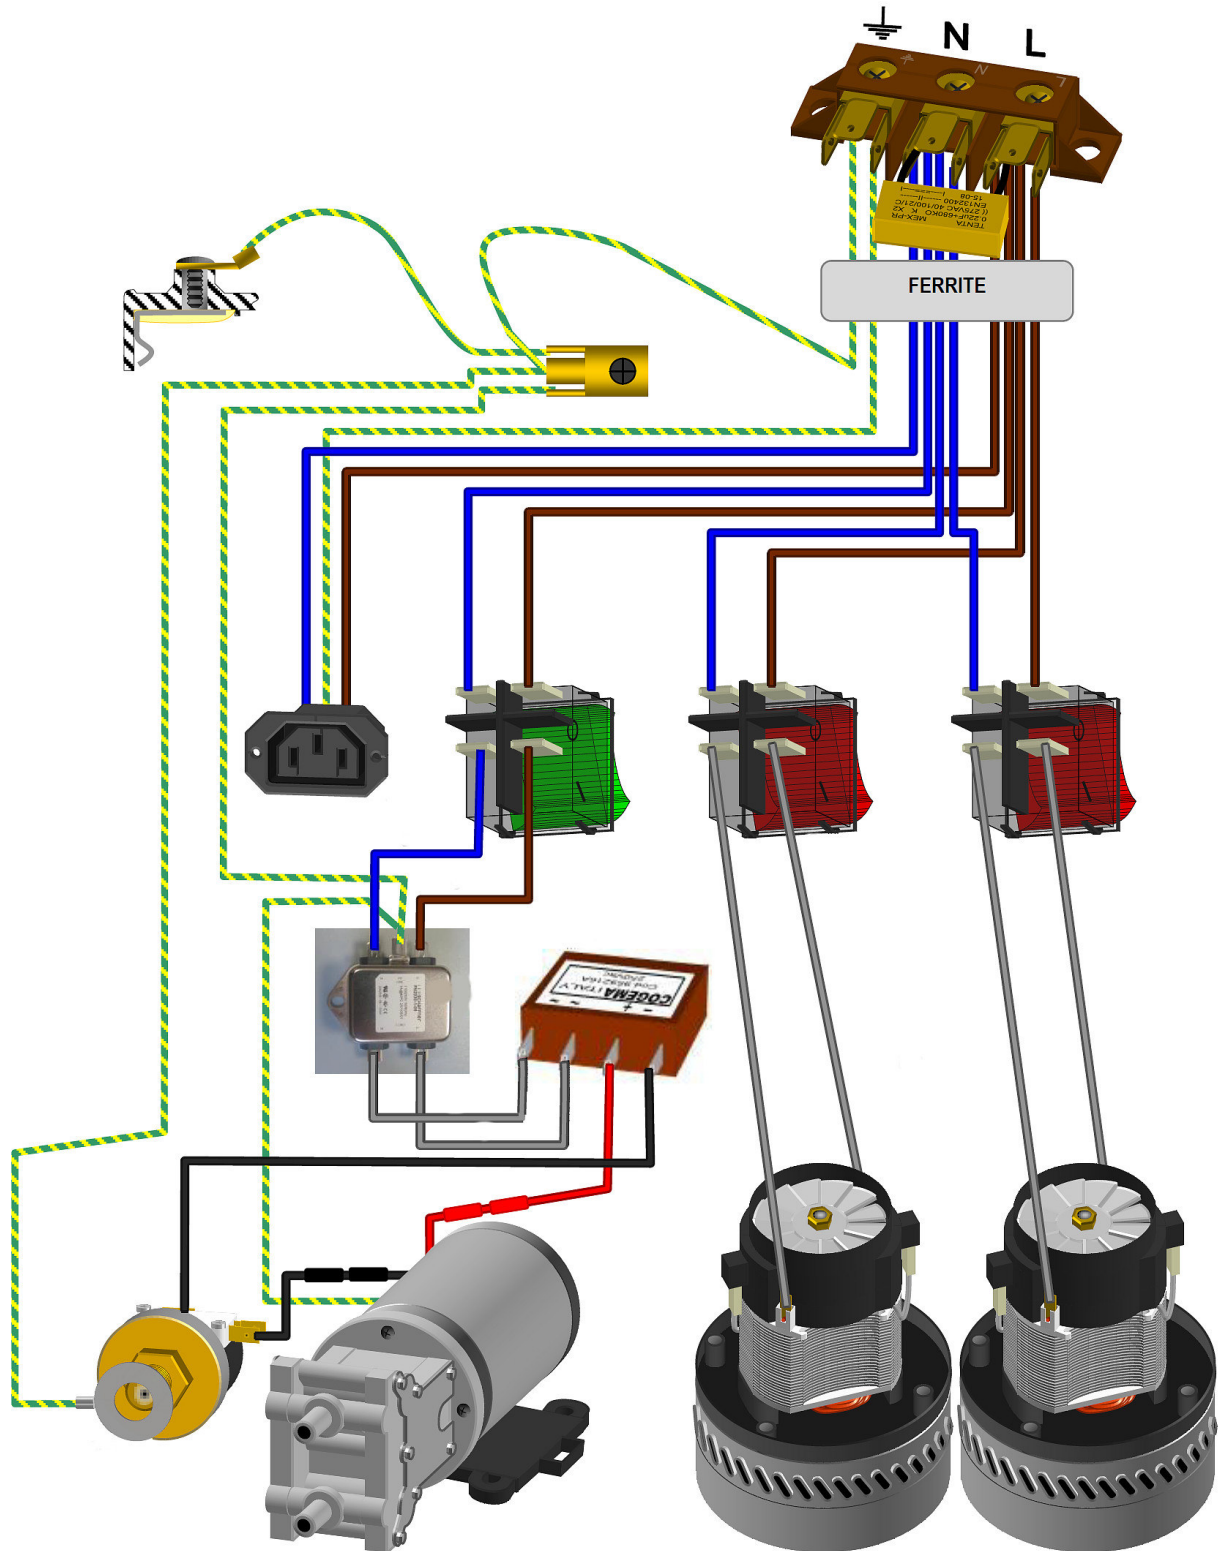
Verdrahtungsplan flexCAT 262 PD
